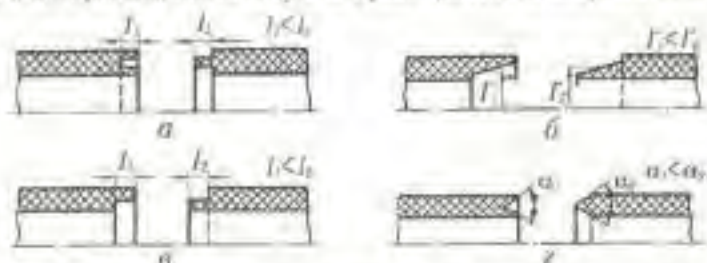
Конструкції розробки крамок труб під зварювання тертям
